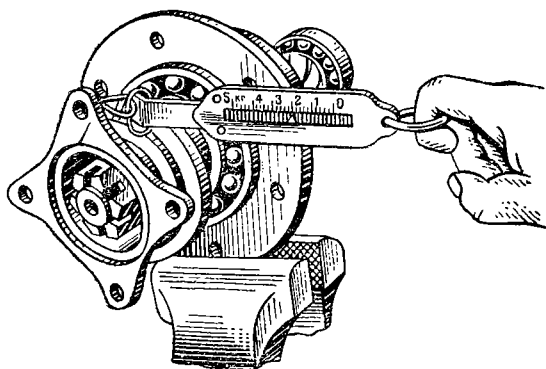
Проверка затяжки подшипников ведущей шестерни
